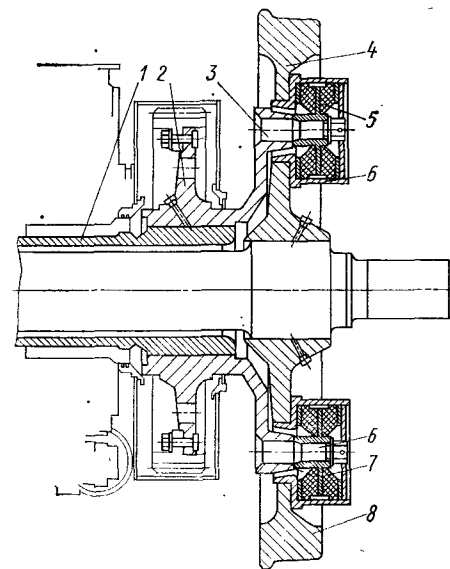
Конструкция опорно-центрального тягового привода с резинометаллическими амортизаторами:
